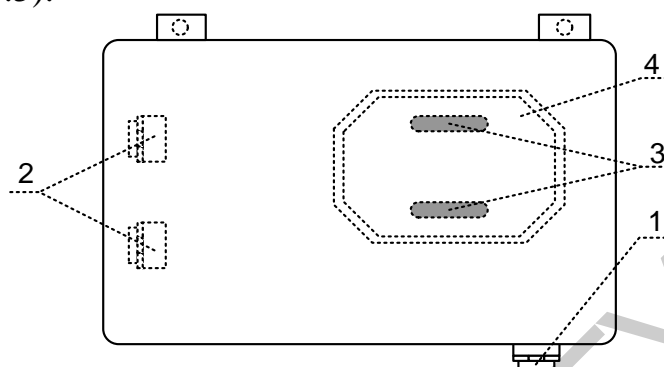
Схематический чертёж переключателя ПРИЕМ-ПЕРЕДАЧА:
